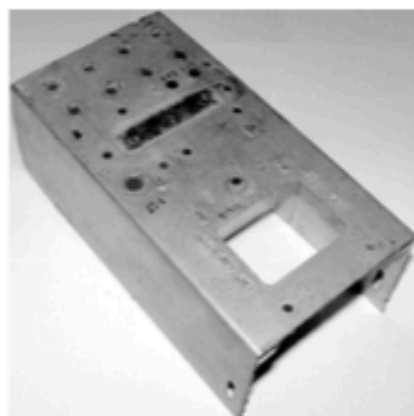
Вид заготовки из шасси блока усиления мощности радиостанции “Кама-С”. Вид сверху
